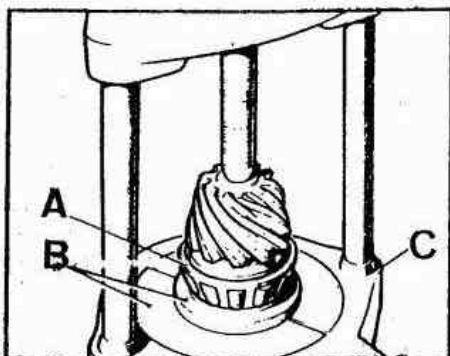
Montaje del cojinete de cabeza del piñón de ataque
